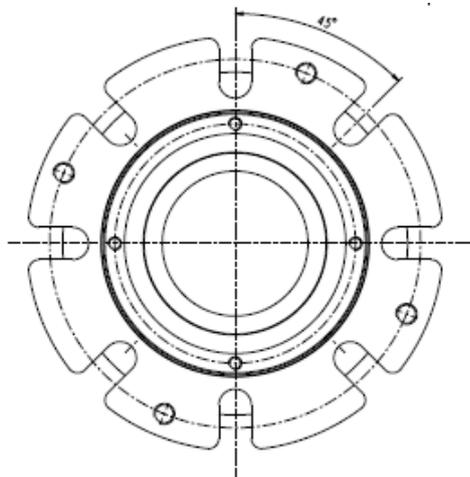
HD202 Ajuste de juego axial – ajuste de la caja de rodillos (Pos. CR)
